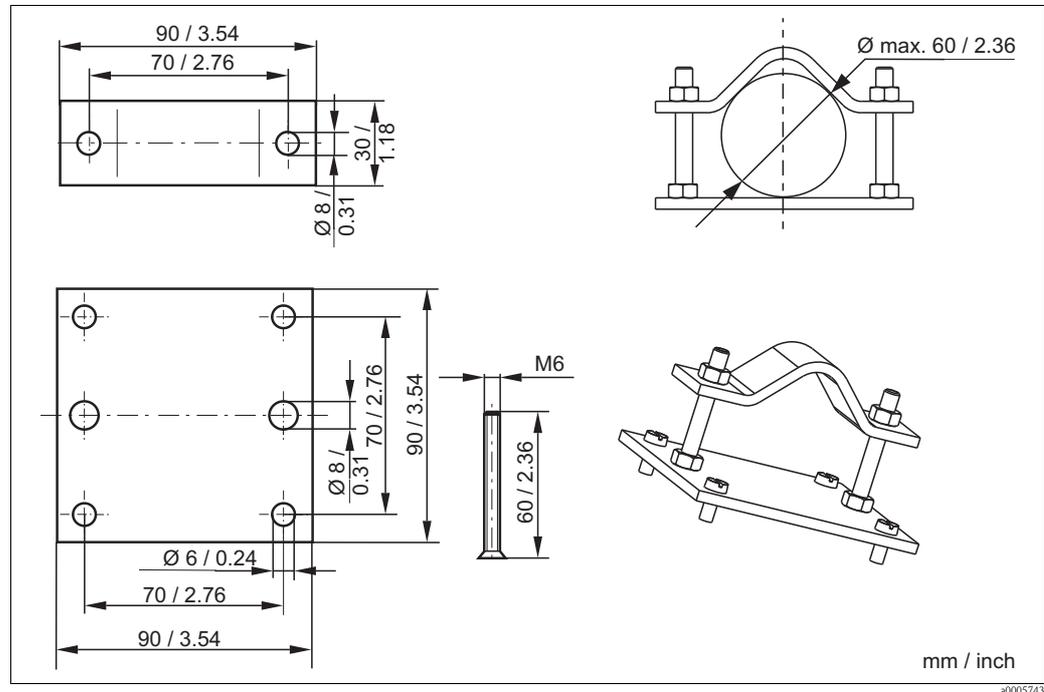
Kit de montage pour la fixation sur tube ou mât
